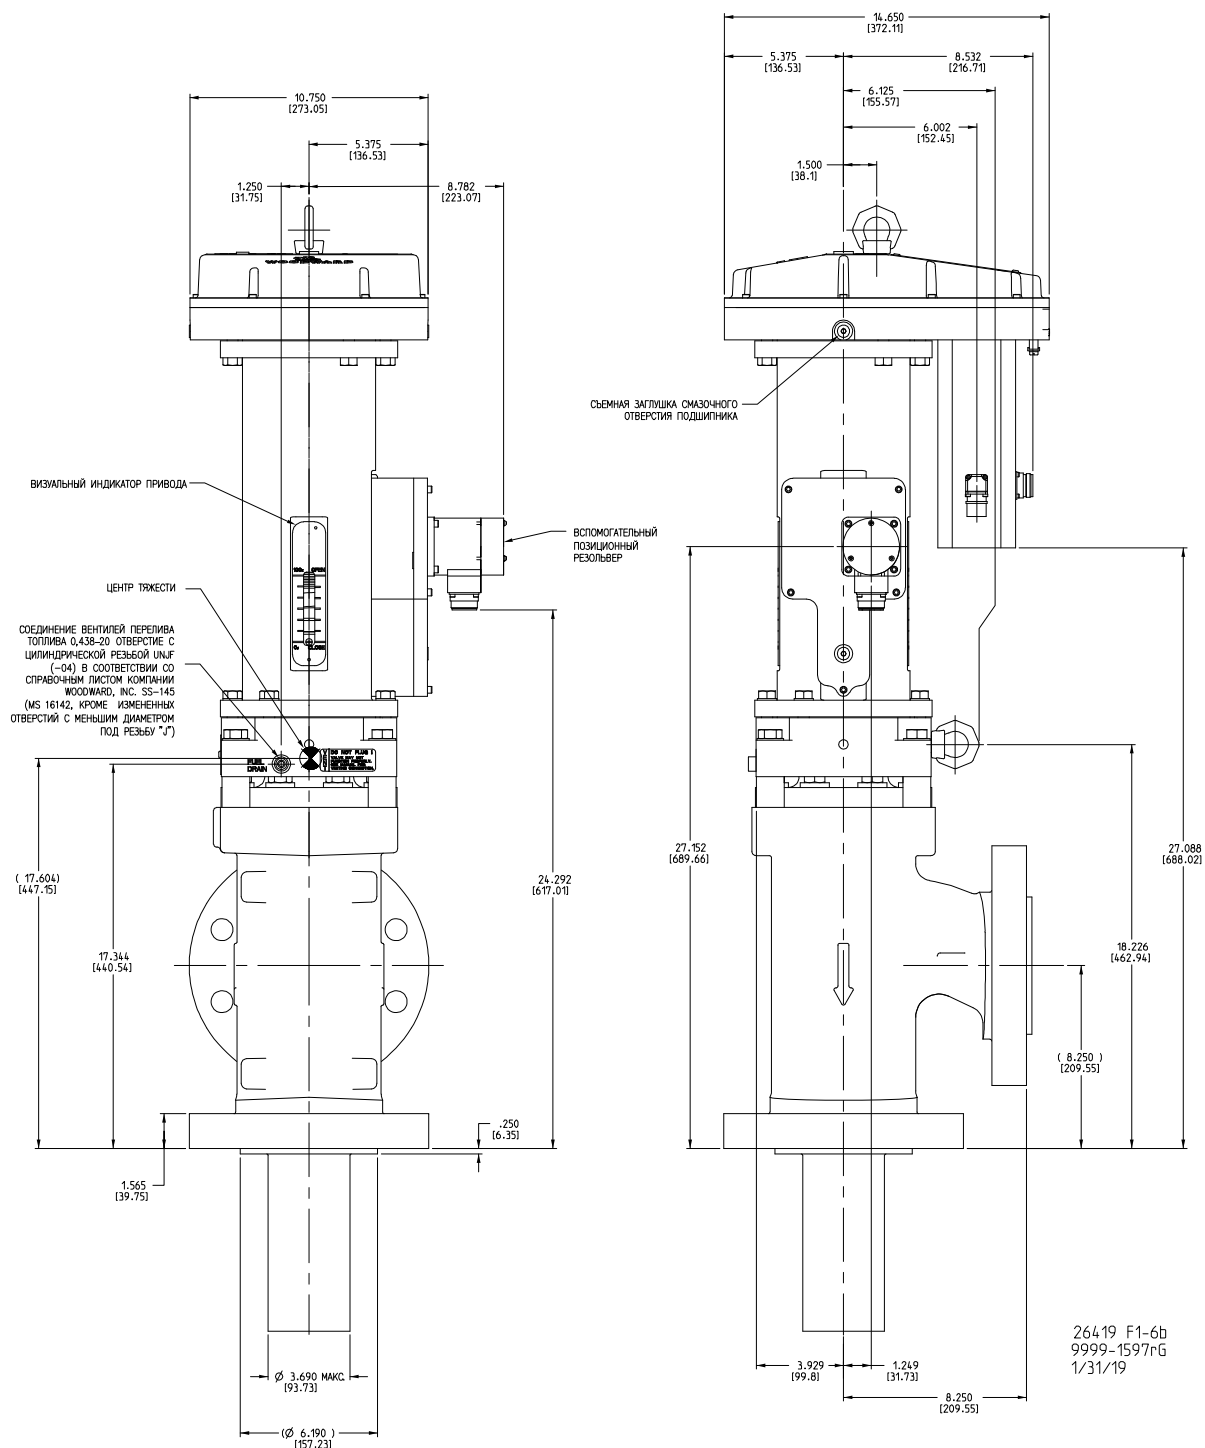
Габаритный чертеж (4-дюймовый клапан LESV класса 600)
